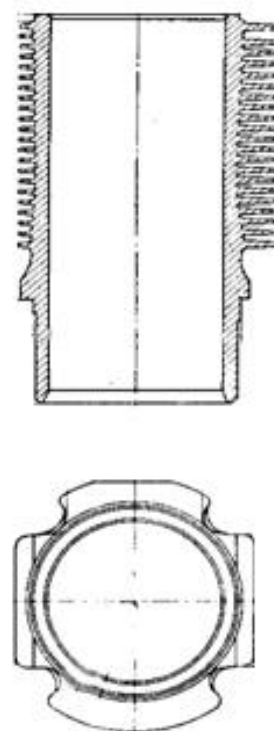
Цилиндр тракторного двигателя воздушного охлаждения
